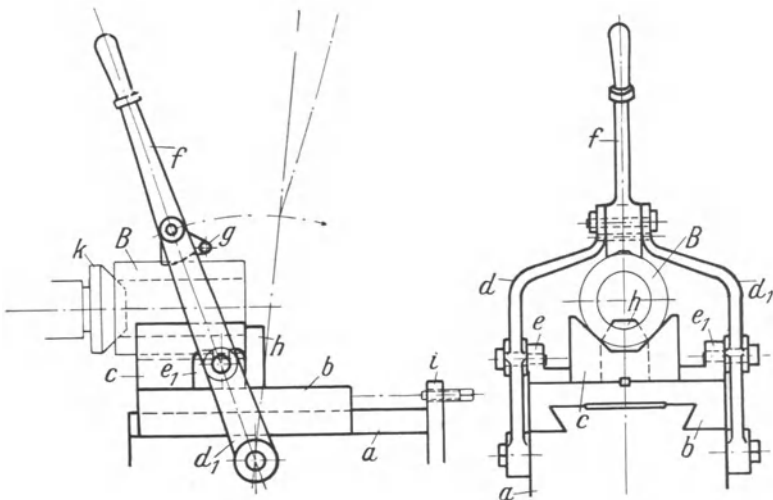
Fräsvorrichtung für das Ausfräsen der inneren Kanten an Buchsen.
